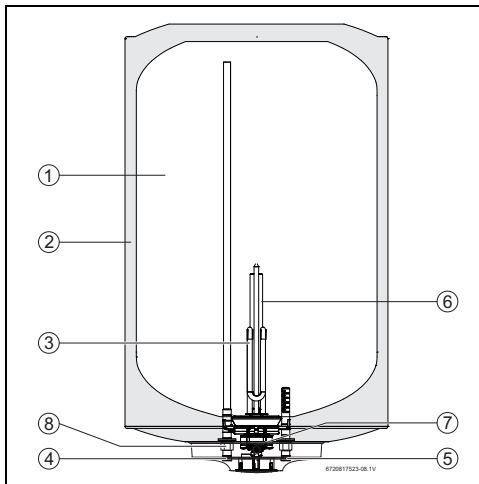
Конструкция бака (здесь: Tronic 2000 T)
